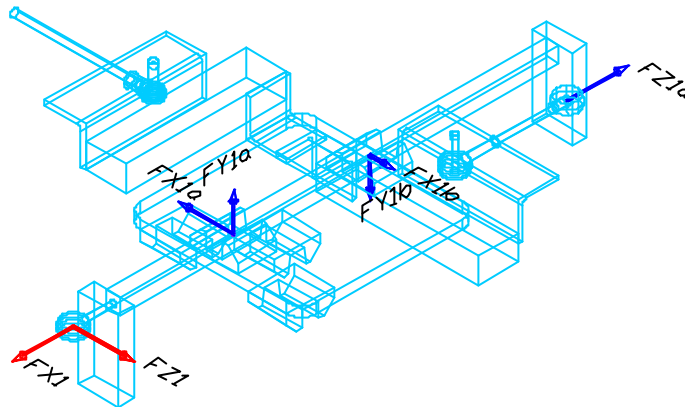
Le forze generate sull'asse Z1 rispetto alla piastra di collegamento dall'imbarco per desorbimento
